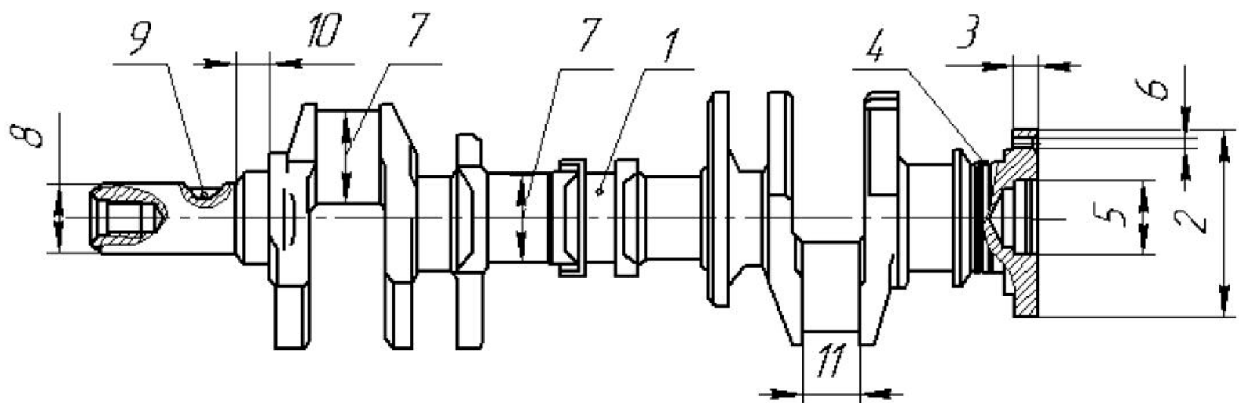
Основні дефекти колінчастого валу на прикладі двигуна ЗІЛ-130: 1 – вигин валу; 2 – спрацьовування зовнішньої поверхні фланця; 3 – биття торцевої поверхні фланця; 4 – спрацьовування мастилозгінних канавок; 5 – спрацьовування отвору під підшипник; 6 – спрацьовування отворів під болти кріплення маховика; 7 – спрацьовування корінних і шатунних шийок; 8 – спрацьовування шийки під шестерню і маточину шківів; 9 – спрацьовування канавки шпонки по ширині; 10 – збільшення довжини передньої корінної шийки; 11 – збільшення довжини шатунних шийок
